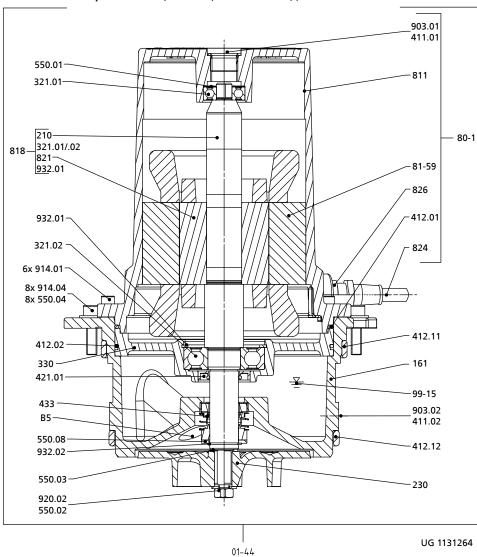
Покомпонентный сборочный чертеж mini-Compacta U60, U100, UZ150 — рабочая часть
